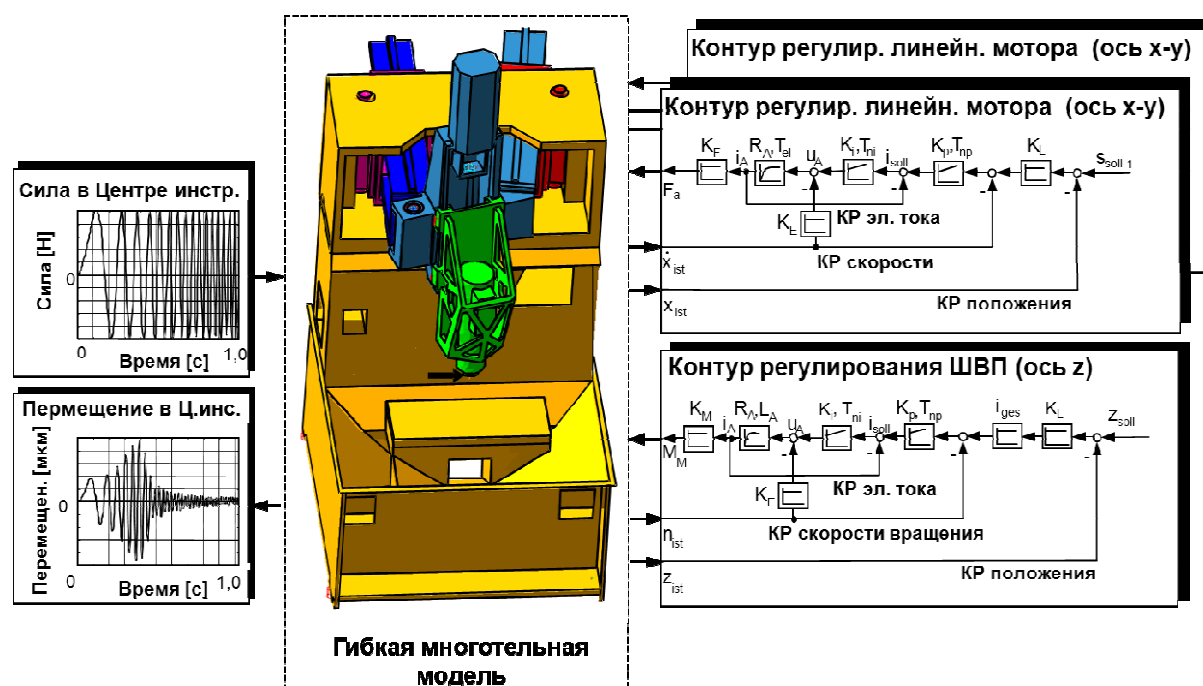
МТ-модель фрезерного станка с контурами регулирования
